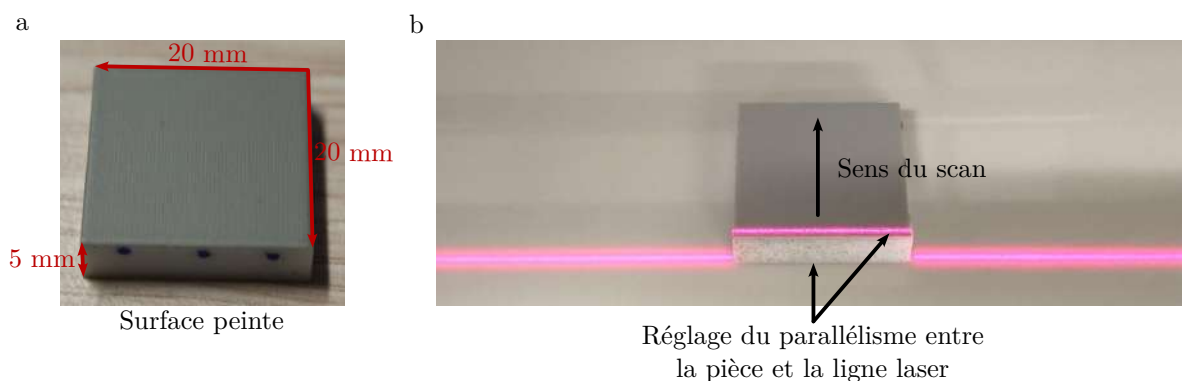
Illustration des mesures sur pièce test pour proposer des tolérances
